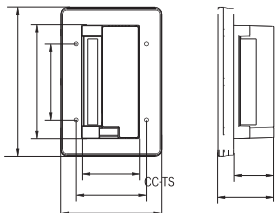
Dimensions du régulateur centralisé (unité : mm)
